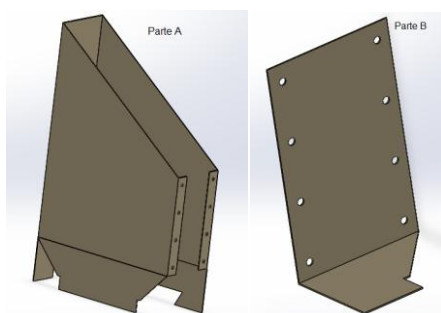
Partes do porta-revistas (desenho em SolidWorks)
